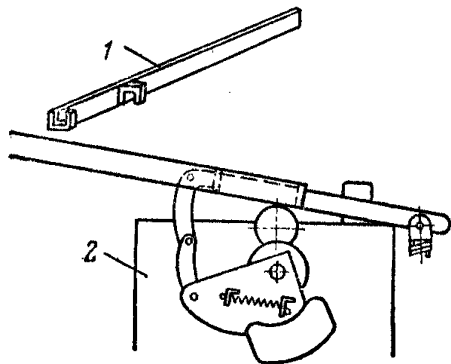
Рычаг для расцепления пружин привода ПП-67:
